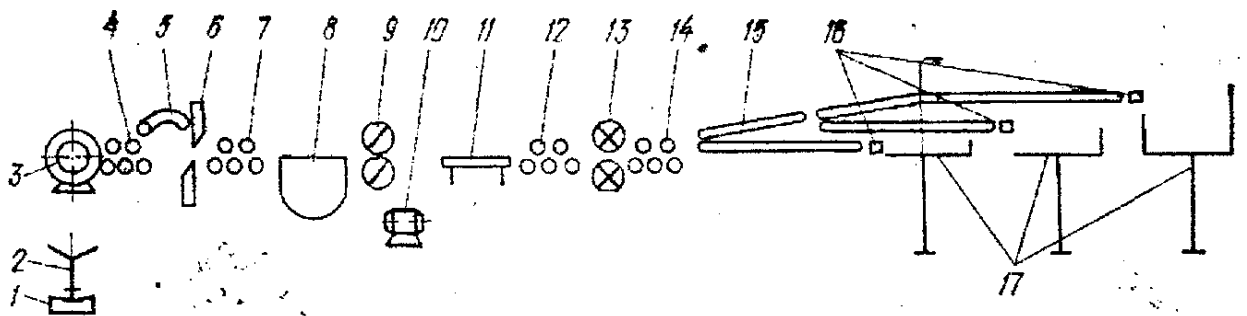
Схема агрегату поперечного різання холоднокатаних штаб
